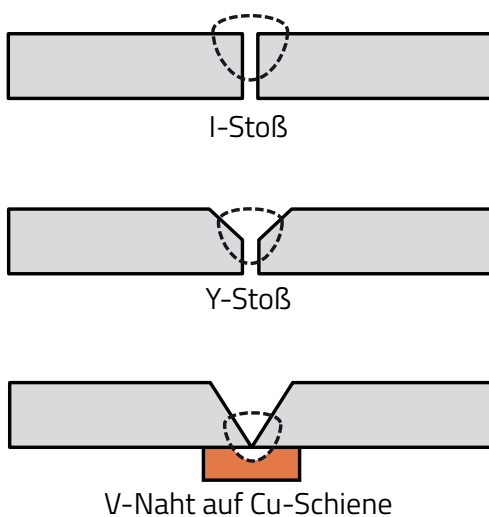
Typische Fugenformen und Badsicherungen beim maschinellen MSG-Schweißen
